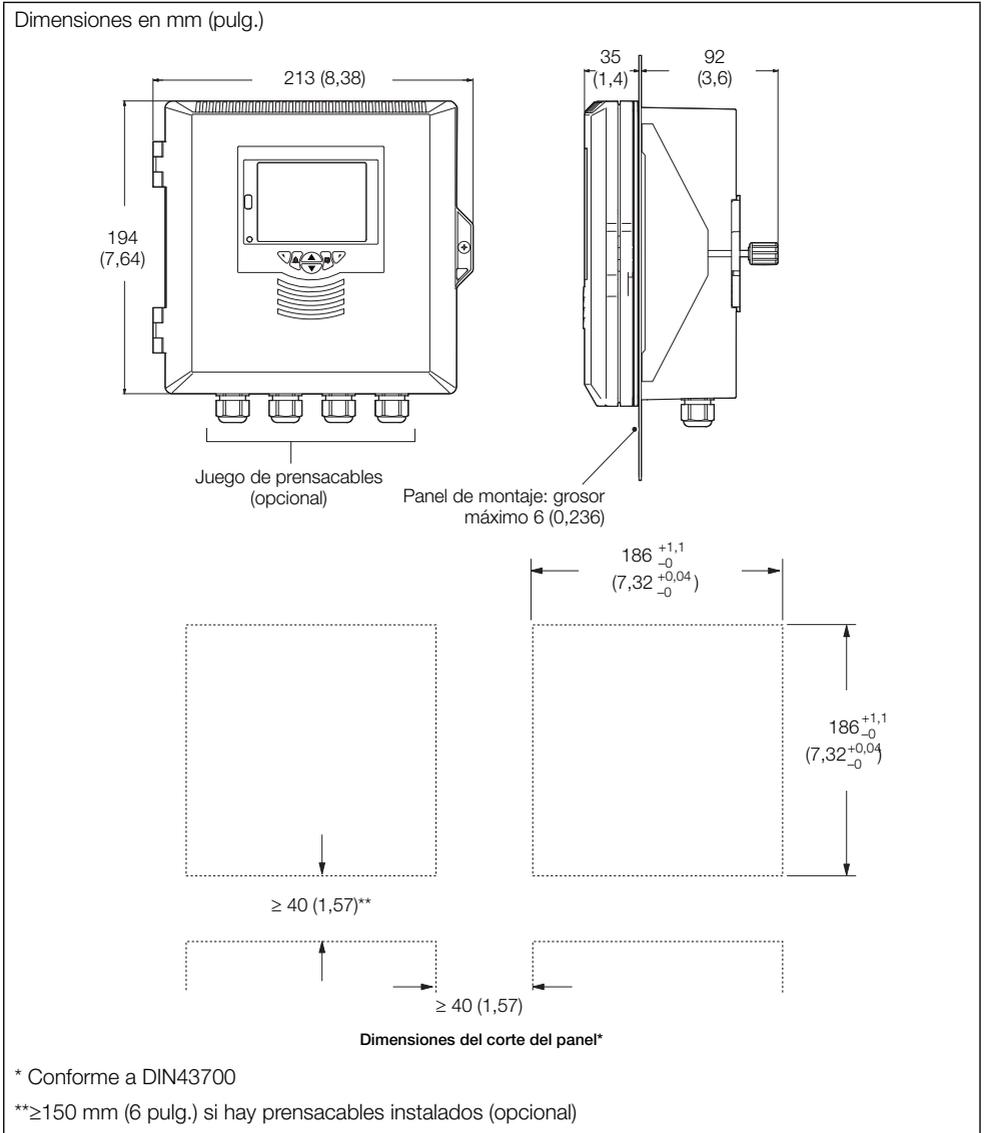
Opción de montaje en panel del ControlMaster CMF310
